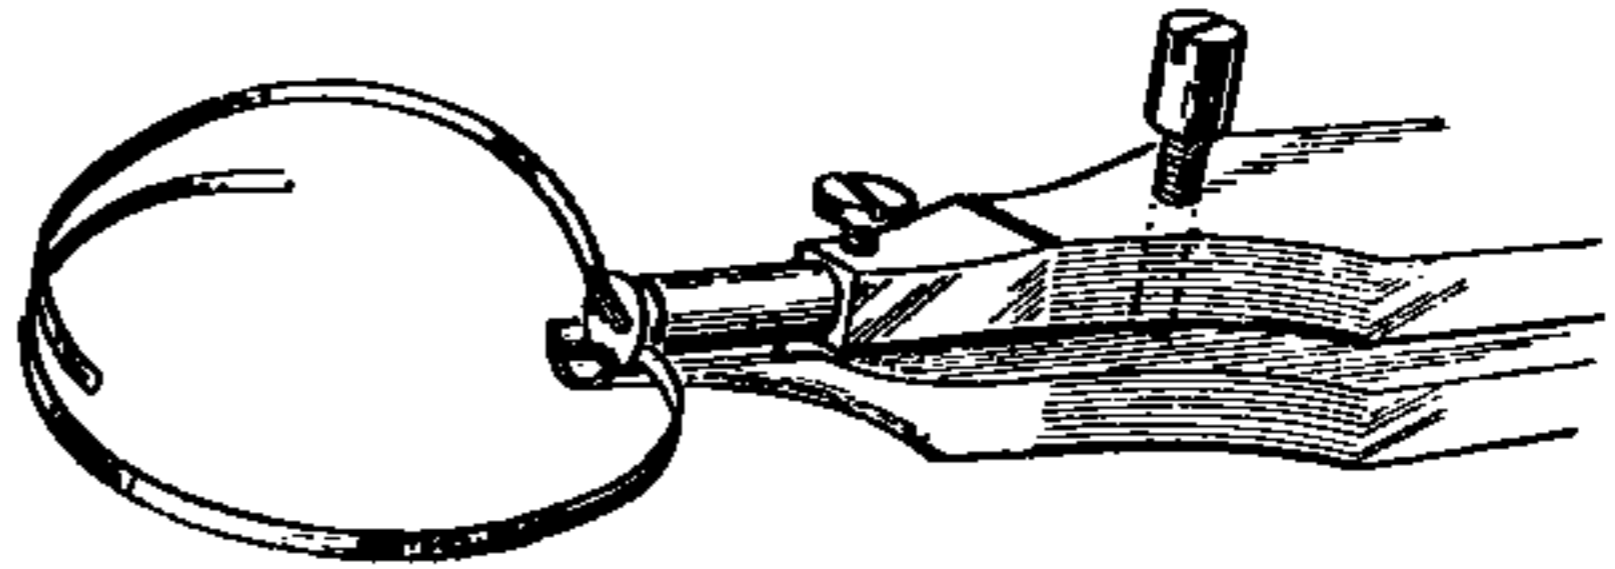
Pinzette speciali per formare la spira superiore. Piegatura verso l'alto della spira superiore.
